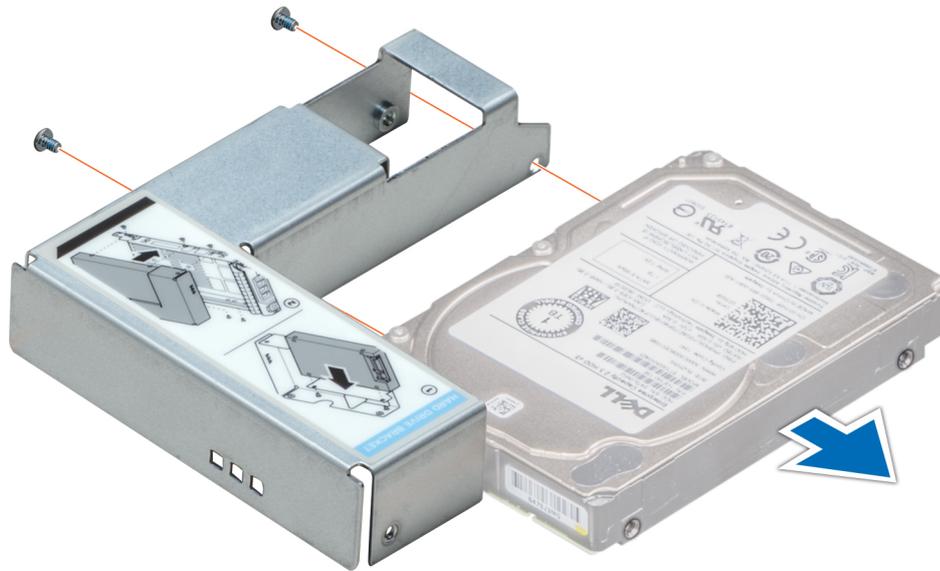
Entfernen eines 2,5-Zoll-Laufwerks aus einem 3,5-Zoll-Laufwerksadapter
